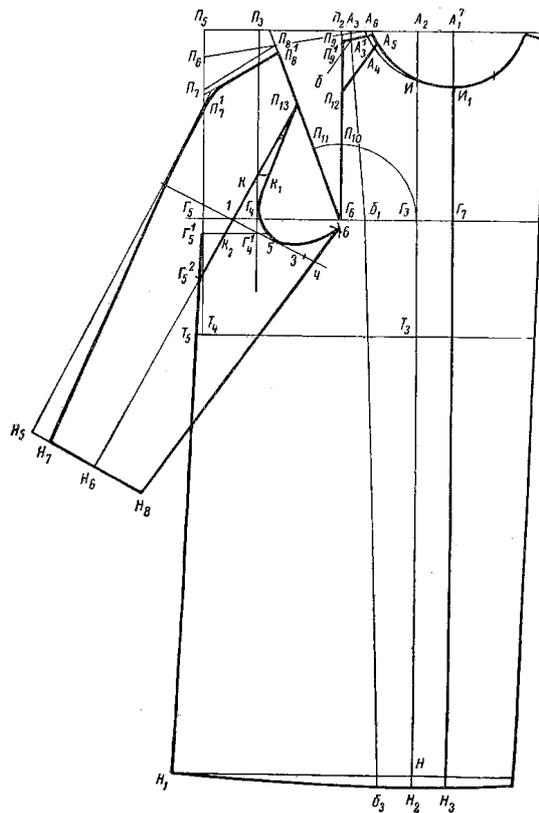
Чертеж полочки плаща из полихлорвиниловой пленки
